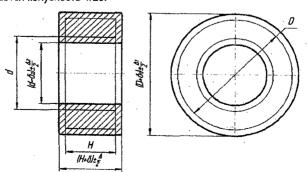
Схема назначения припусков и допусков для поковок 3-ей группы
